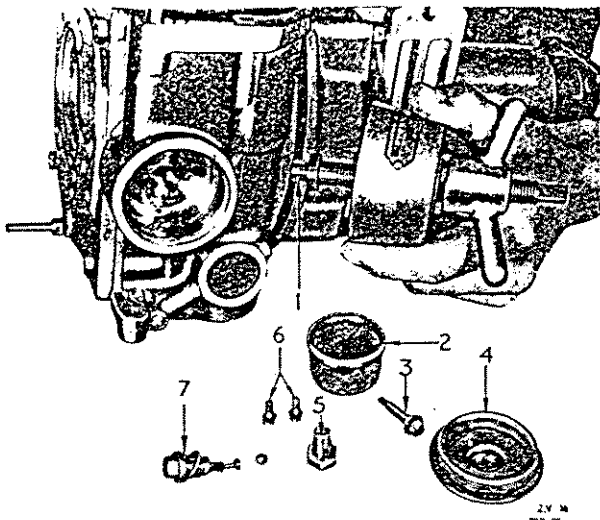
Anwendung des Werkzeuges Nr. L.183 A, bevor Teil 1 in den Pumpenkörper geschraubt wird.
